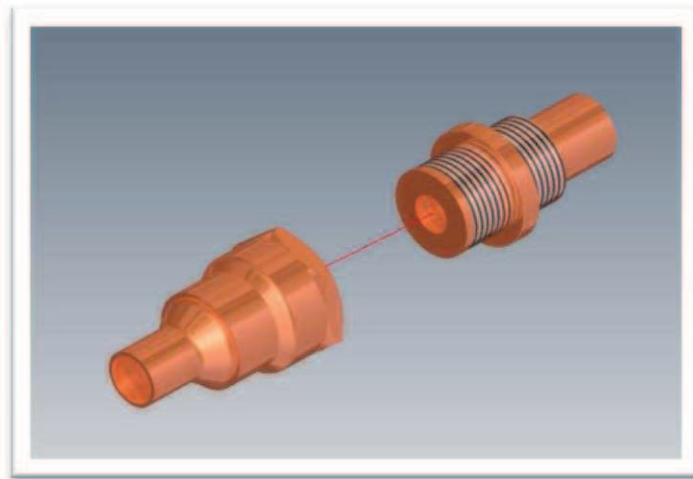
Ensamble del cuerpo de la válvula con la tuerca unión
